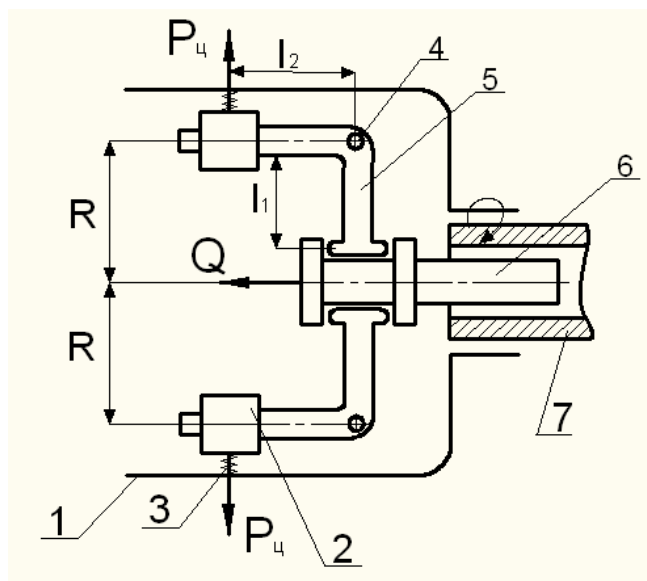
Схема центробежно-инерционного привода токарного станка.
